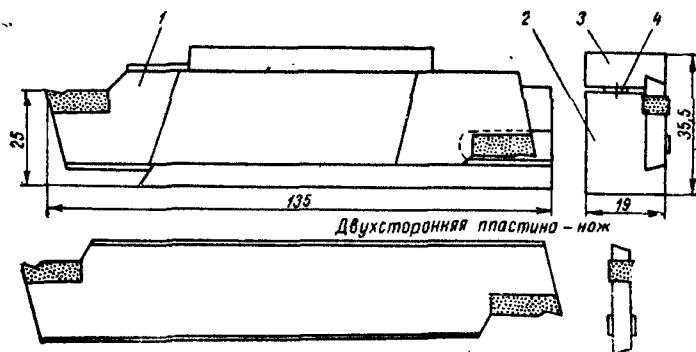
Нормализованный сборный резец с пластинчатым ножом (выпускается Ленинградским коксогазовым заводом).
